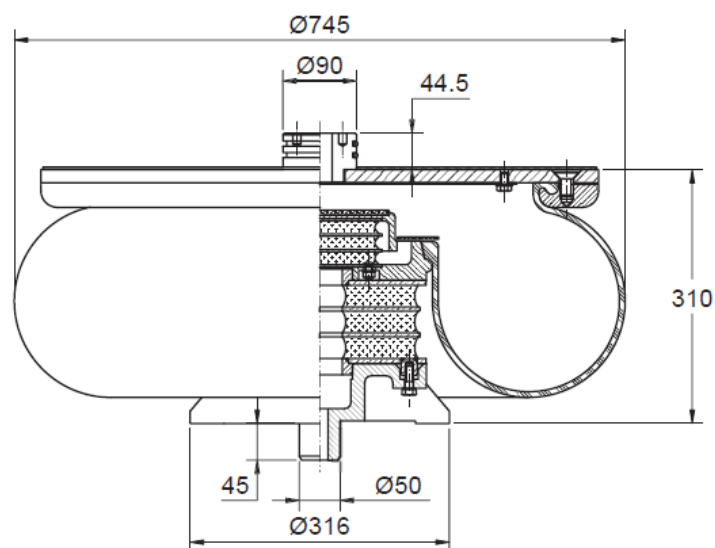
Dimensiones de una suspensión neumática [8]
